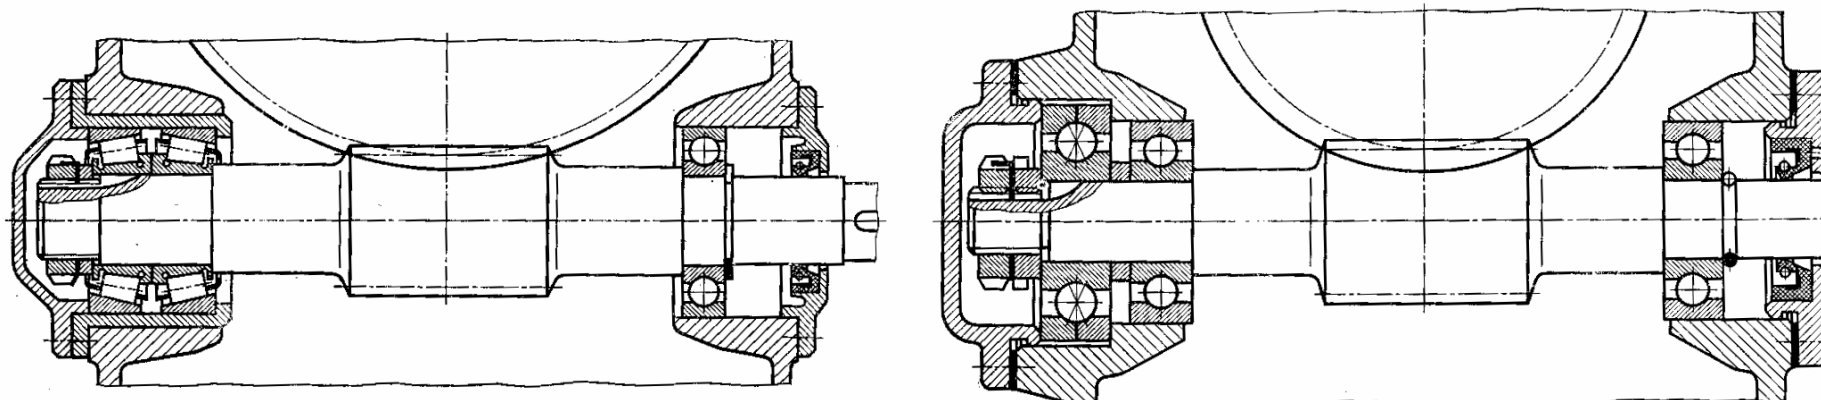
Вал червяка с одним радиальным и двумя радиально-упорными или коническими подшипниками
